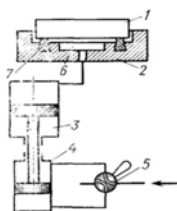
Станочное приспособление с вакуумным приводом с применением пневмоцилиндра
